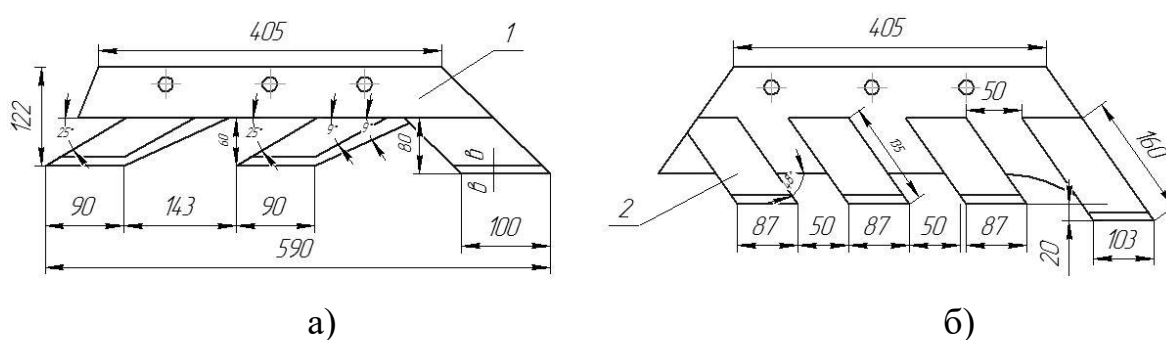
Сварные зубчатые лемеха: 1 – тело лемеха; 2 – свальной зуб
